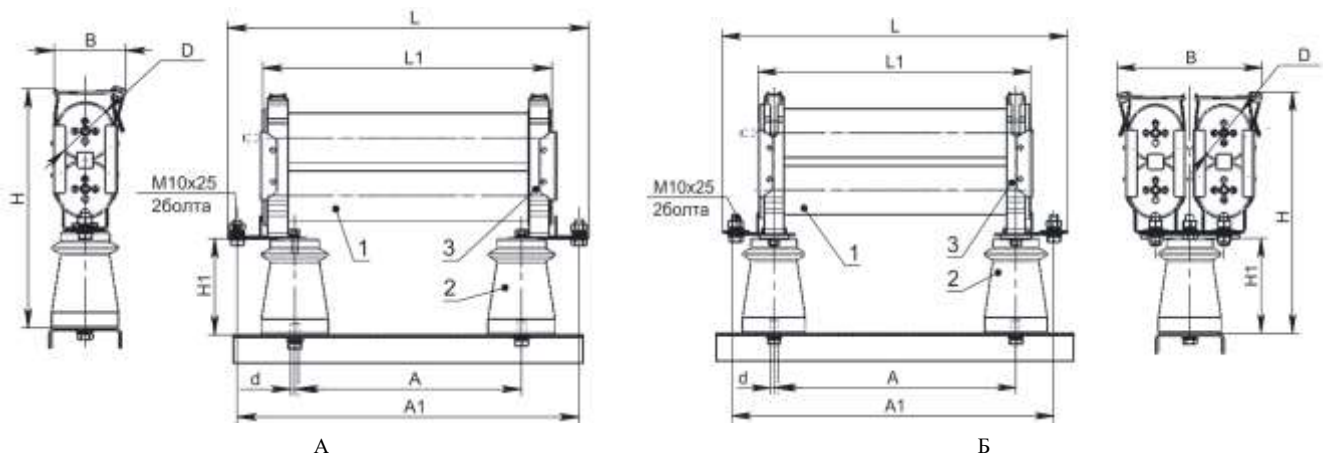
Габаритные и установочные размеры предохранителей ПКТ-103, ПКТ-104.
